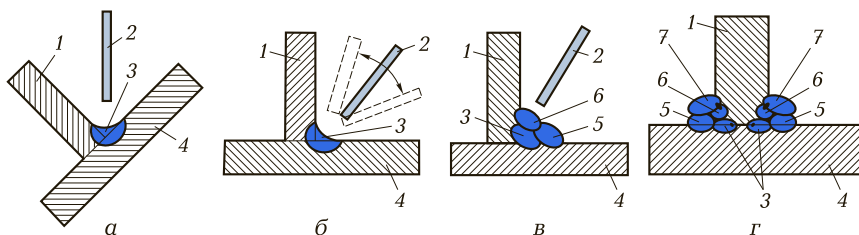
Сварка угловых соединений тавровых балок:
